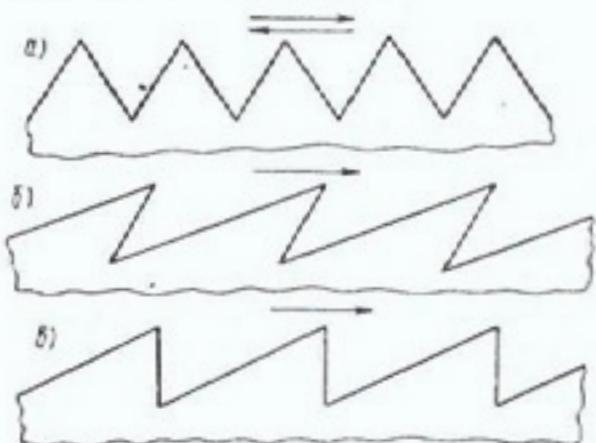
Профили зубьев пилы: а — для поперечного распиливания; б — для продольного распиливания; в — для смешанного пиления.
